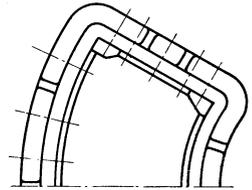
Befestigung des Stahlbesatzes durch Schweißen. Einzelteile eines Schnittes vor dem elektrischen Verschweißen.
